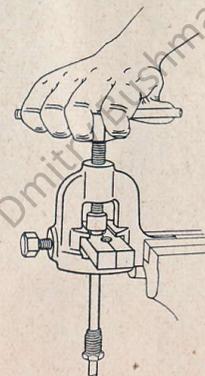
„Ate“-Bördelwerkzeug mit Gewindespindel.
